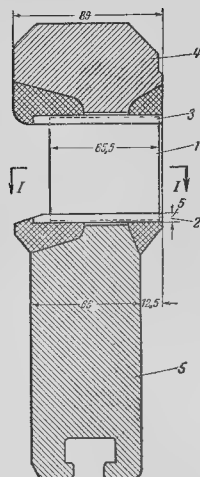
Сварная диафрагма конструкции ХТЗ им. Кирова
